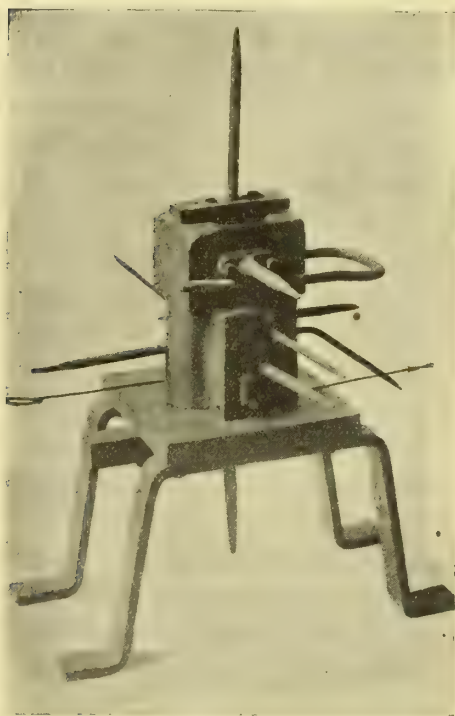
Coquille à mouler l'aluminium, fermée.
